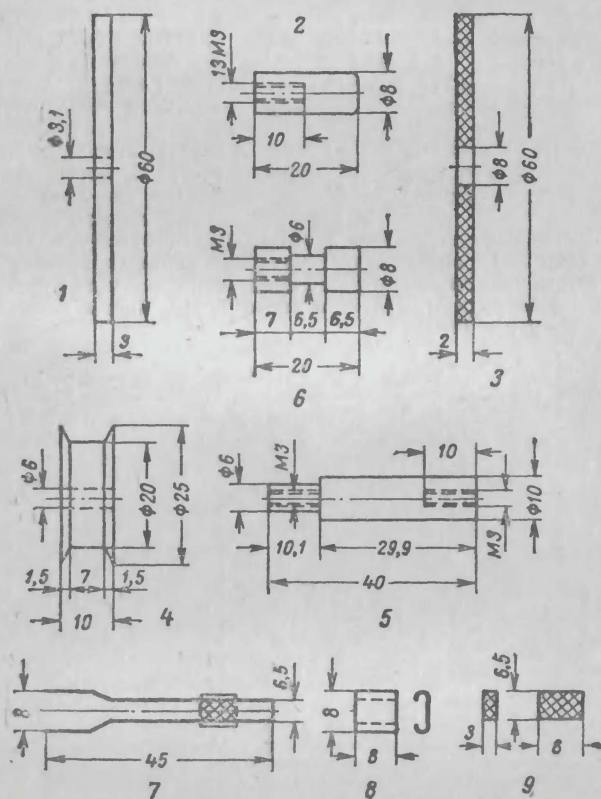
Детали лентопротяжного устройства магнитофонной приставки.
